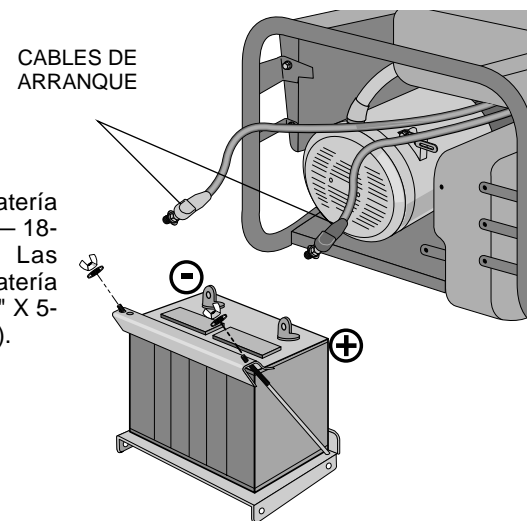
ENSAMBLAJE DEL MARCO DE LA BATERÍA
